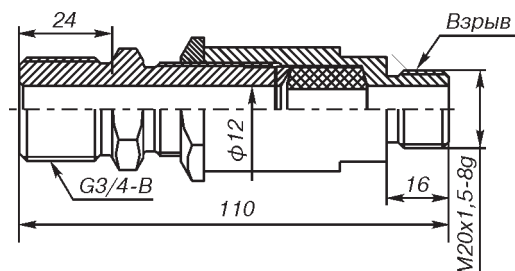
Кабельный ввод для трубного монтажа (ТБ 3/4").
